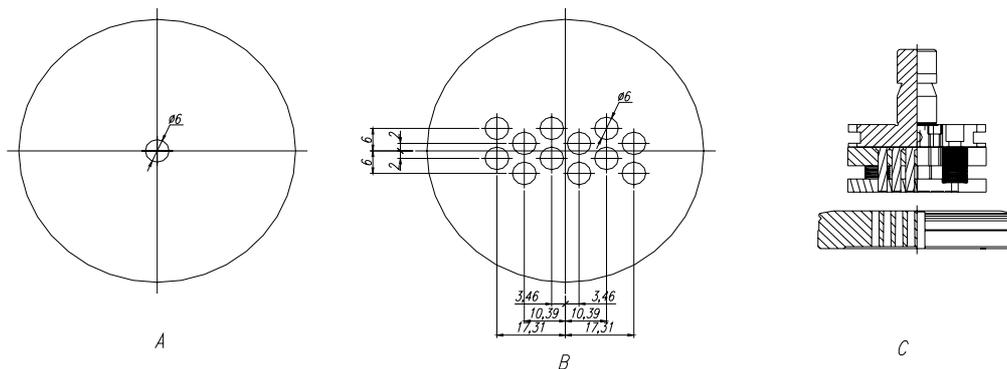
a) Punção único; b) Geometria com doze punções; c) Ferramenta montada em corte
